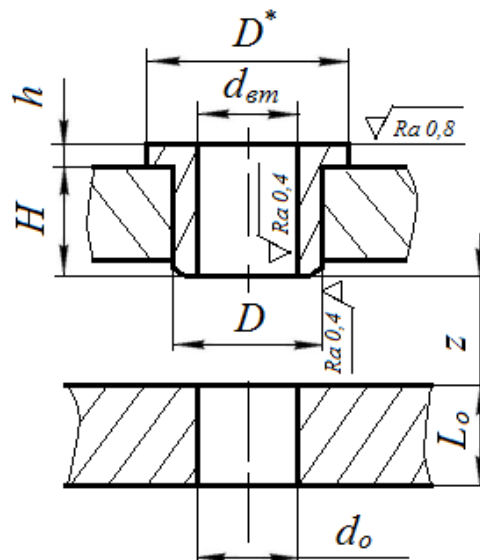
Эскиз упрощенного фрагмента кондуктора с заготовкой, в которой сверлится отверстие (в данном случае, сквозное)
